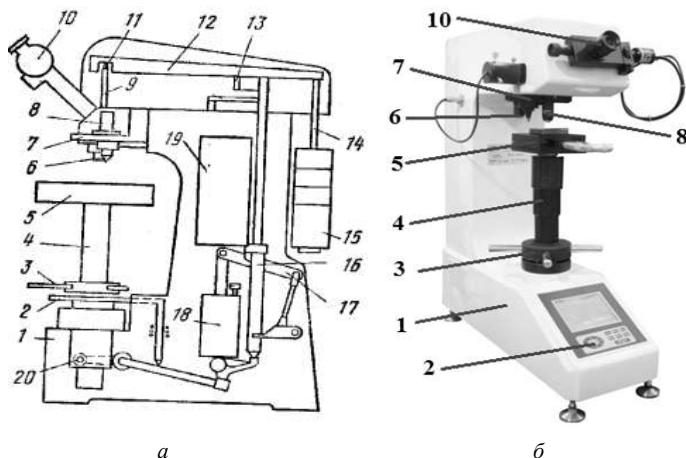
Зовнішній вигляд твердоміру ТП-2 (а) та принципова схема твердоміру HV-10 (б): 1 – станина; 2 – стартова клавіша; 3 – гайка-маховик; 4 – гвинт; 5 – предметний столик; 6 – індентор; 7 – поворотна головка; 8 – об’єктив; 9 – робочий шпindel; 10 – мікроскоп (гвинтовий окуляр-мікрометр); 11, 13 – опори важеля; 12 – важіль; 14 – підвіска для тягарів; 15 – тягарі; 16 – підйомний шток; 17 – ручка взводу приводу тягарів; 18 – привід тягарів з масляним амортизатором; 19 – тягар для противаги; 20 – електродвигун
